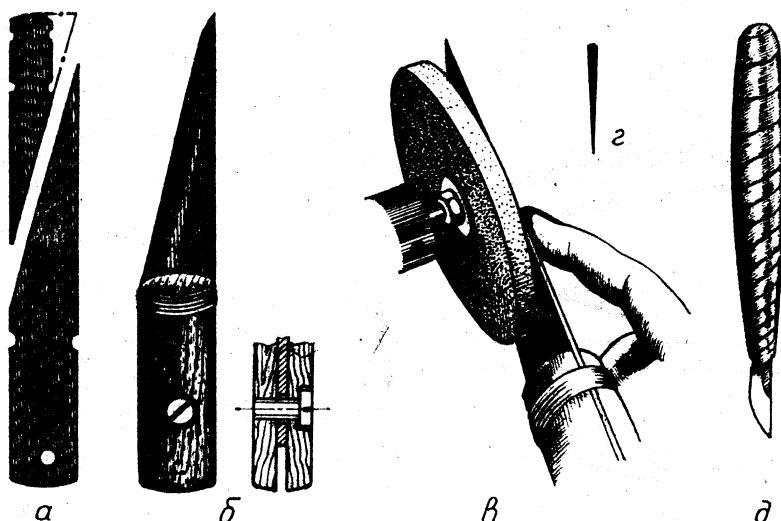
Ножи для резьбы: а — изготовление ножей из ножевочного полотна; б — устройство ручки; в — заточка ножа; г — поперечное сечение ножа; д — маленький ножик из надфilia
